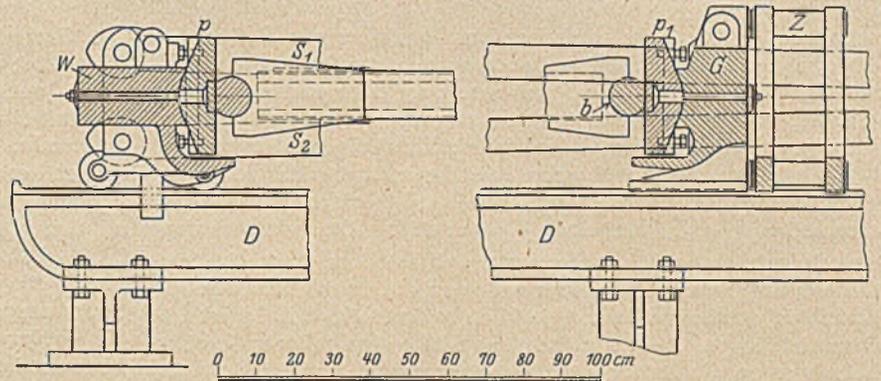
Befestigung der Stabenden in der Werderschen Druckmaschine.
